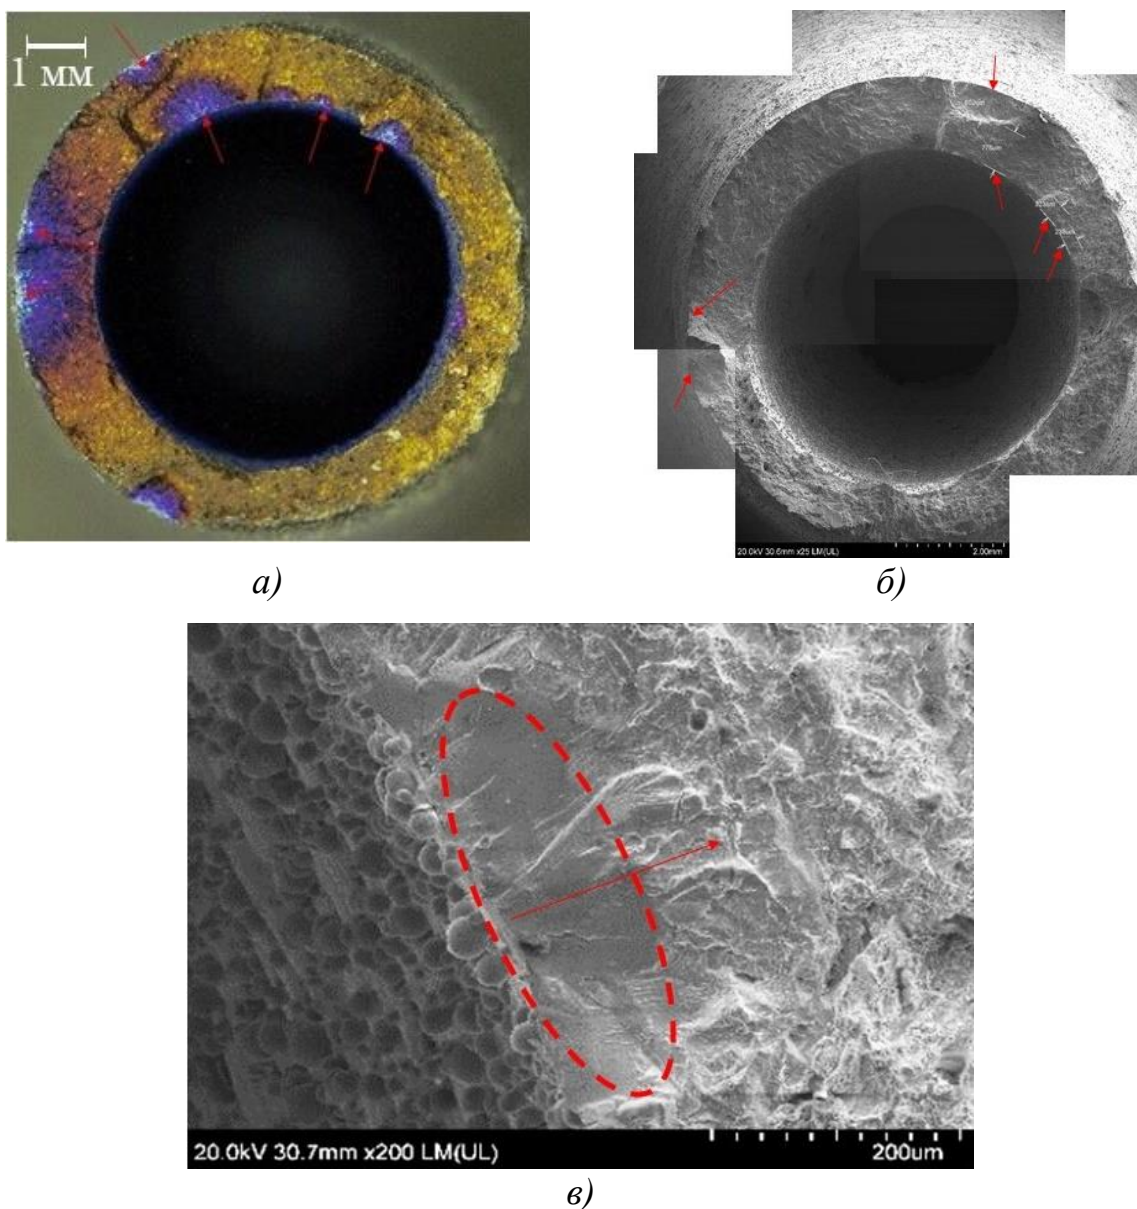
Общий вид (а, б) поверхности разрушения тонкостенного образца с экспонируемой поверхностью, очаг разрушения (в)
